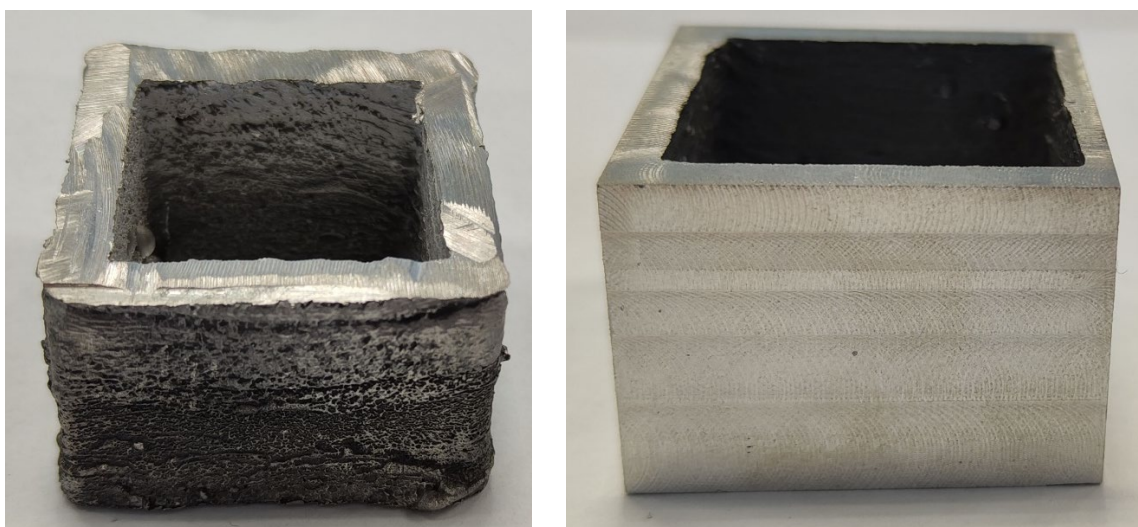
Заготовка в виде трубы квадратного сечения до и после механической обработки
